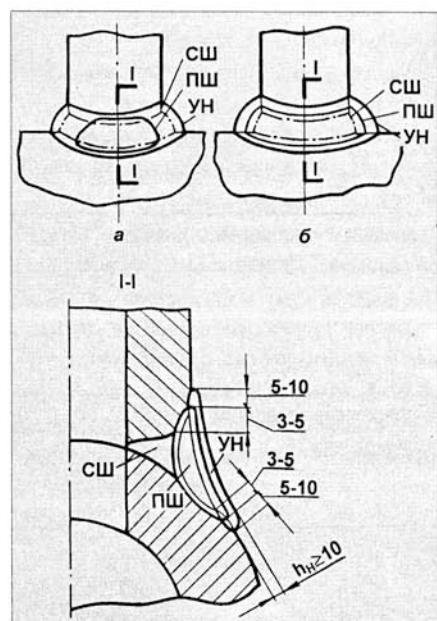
Рекомендуемые формы симметричной усиливающей кольцевой наплавки и подварочных швов (УН — усиливающая наплавка, ПШ — подварочный шов): а — местный ПШ; б — кольцевой ПШ
